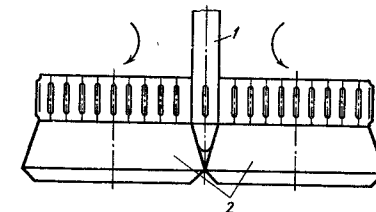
Схема формообразования баллистического заострения дюбелей: 1 — дюбель; 2 — валки
